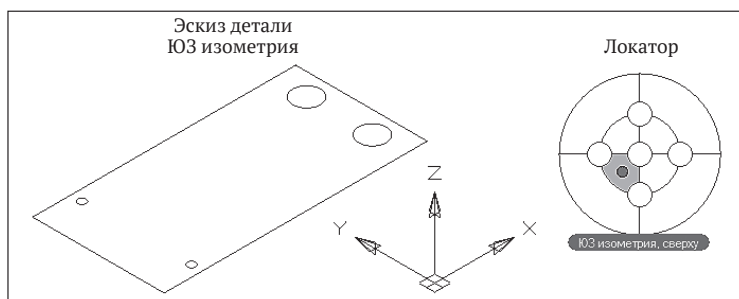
Эскиз детали «Перемычка» в ЮЗ изометрии
